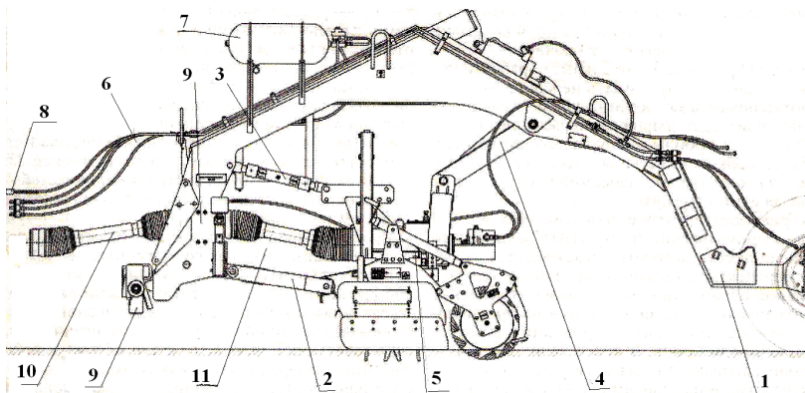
Адаптер почвообрабатывающий (вид сбоку): 1 – рама; 2 – сеялка; 3 – талп; 4 – рычаг; 5 – почвообрабатывающая машина; 6 – гидрооборудование; 7 – пневмооборудование тормозной системы; 8 – соединительная головка пневмосистемы трактора и агрегата; 9 – навеска; 10 – контрпривод; 11 – вал карданный
